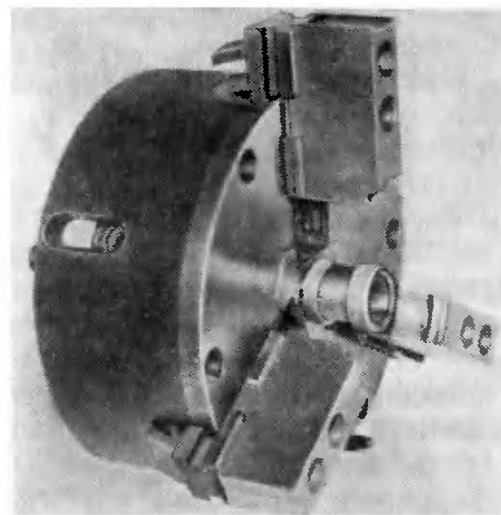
Общий вид механизированного патрона для станка типа АТПр-2М12У.
